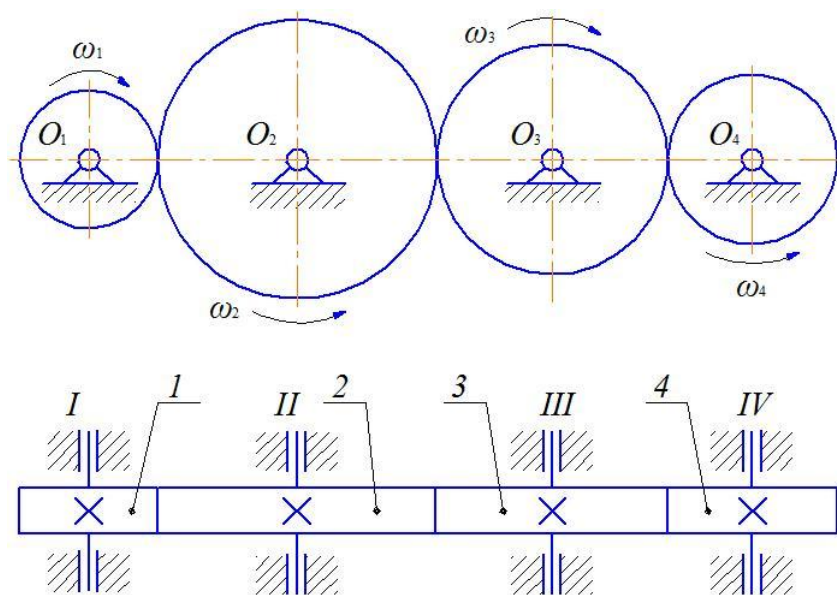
Рядный (рядовой) зубчатый механизм
